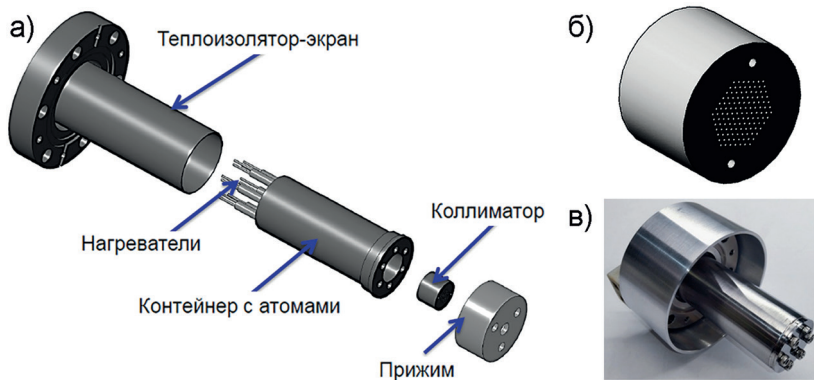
Источник атомов с вневакуумными нагревателями и комбинированным теплоизолятором-экраном: сборочные единицы источника: фланец DN40CF, теплоизолятор-экран, контейнер с атомами, коллиматор-фильтр, прижим (а); внешний вид коллиматора-фильтра в увеличенном масштабе (б); внешний вид ИНА: детали соединены лазерной сваркой (вид со стороны вакуумной части), установлен коллиматор-фильтр с прижимом (в)
